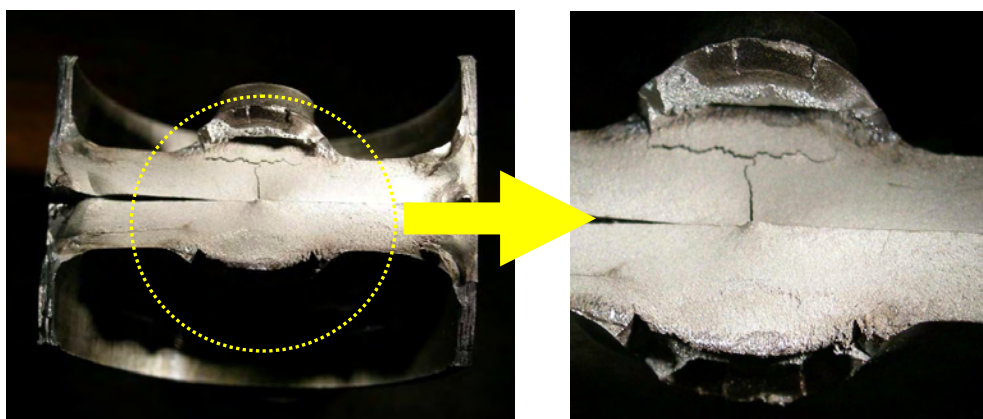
Photo des deux faces du poussoir après ouverture des fissures de fatigue
